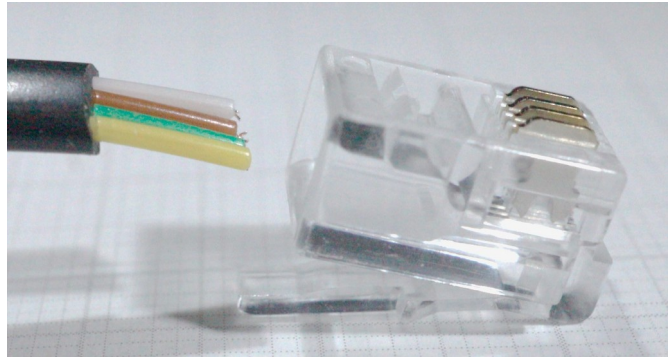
Motorstecker: Kabel in Modular 4P4 Stecker einführen - POLUNG !!!
